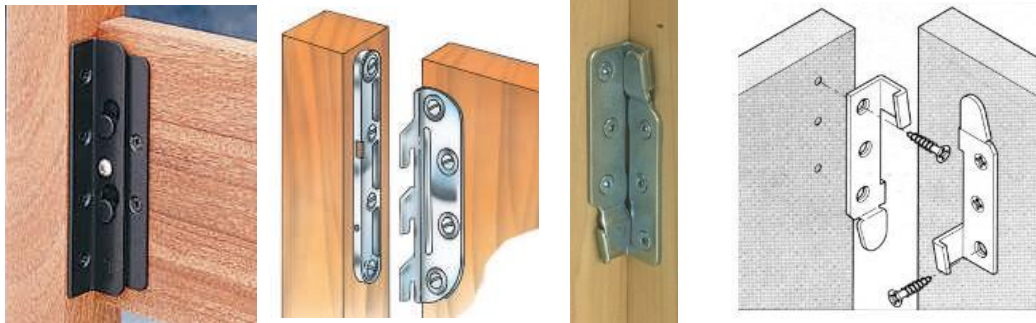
Hettich, Euro köşebent ve montaj şeması (Hettich, 2014)
